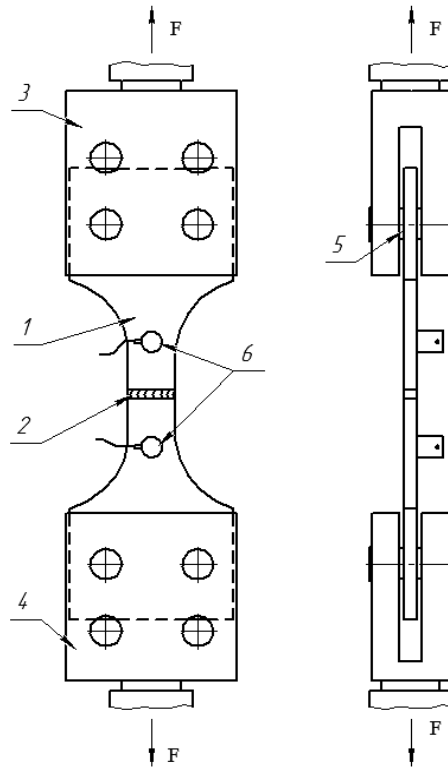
Схема нагружения образца: 1 – образец; 2 – сварной шов; 3 – верхний захват нагружающего устройства; 4 – нижний захват нагружающего устройства; 5 – палец; 6 – ПАЭ
